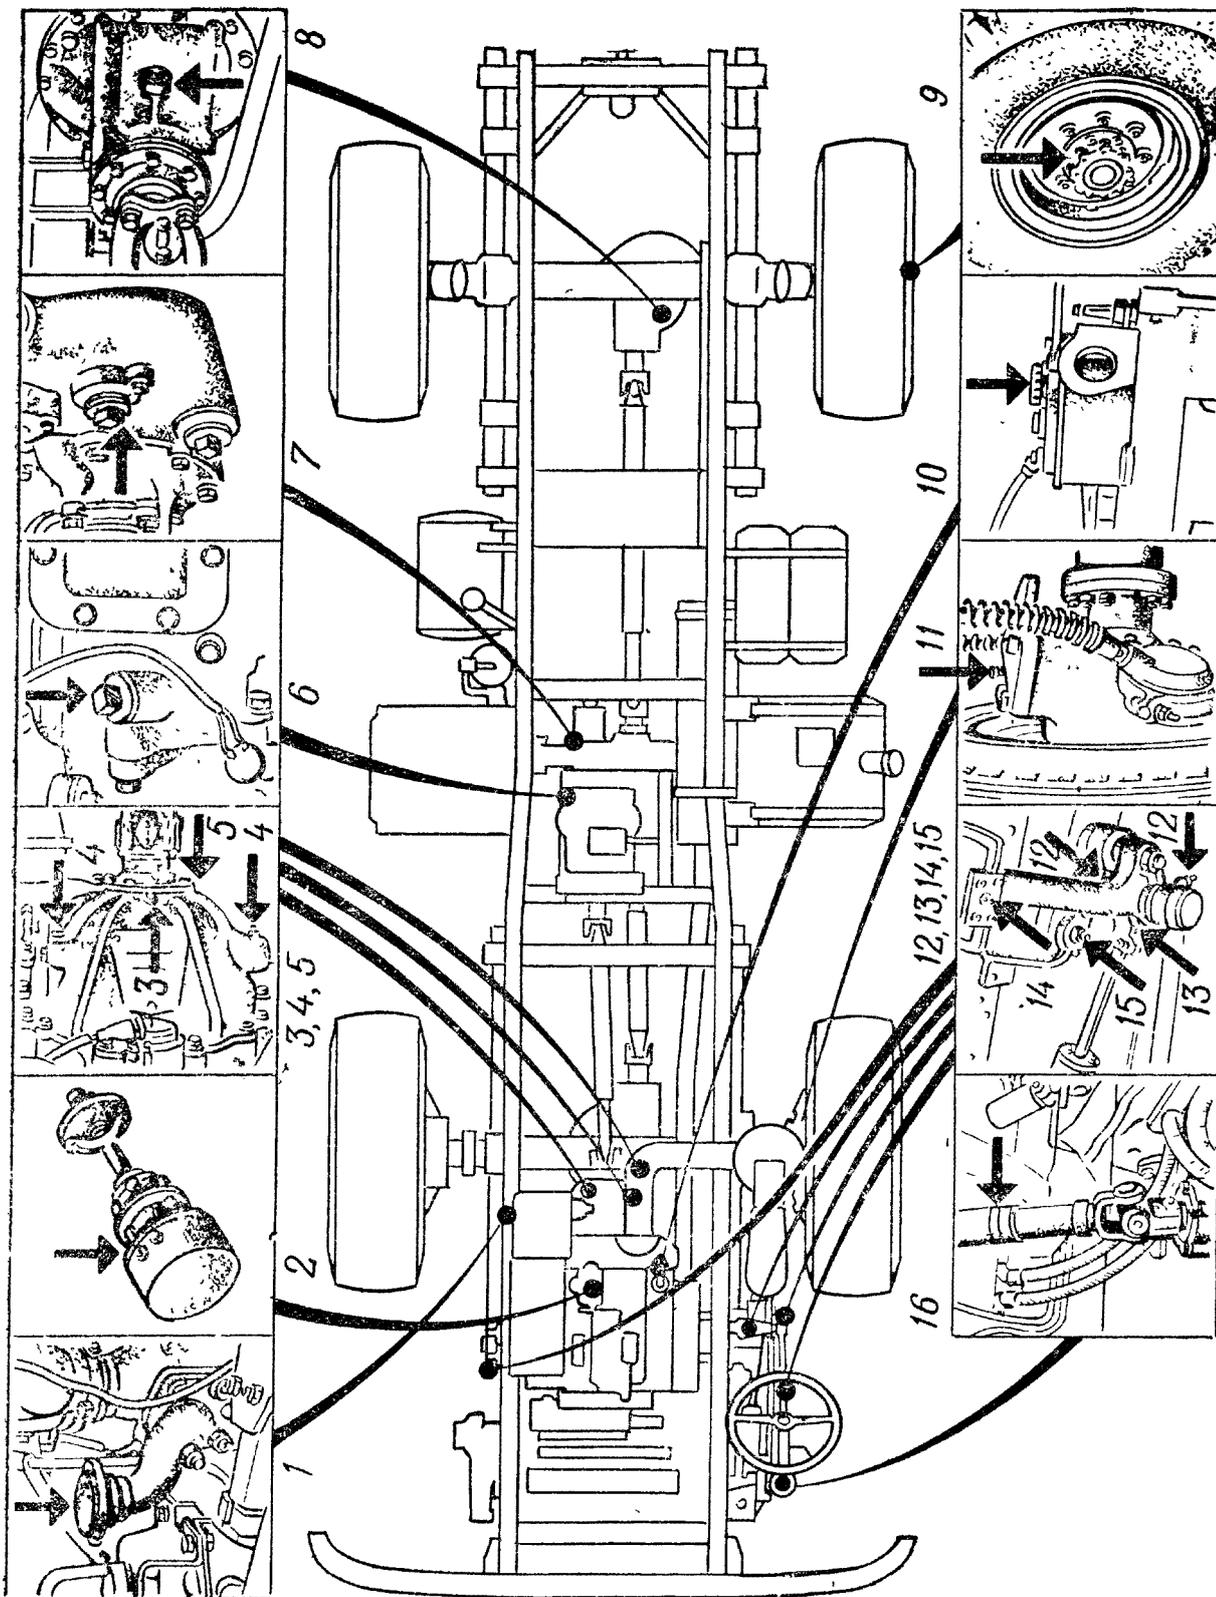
Точки смазки автомобиля. Обозначения см. в таблице смазки
